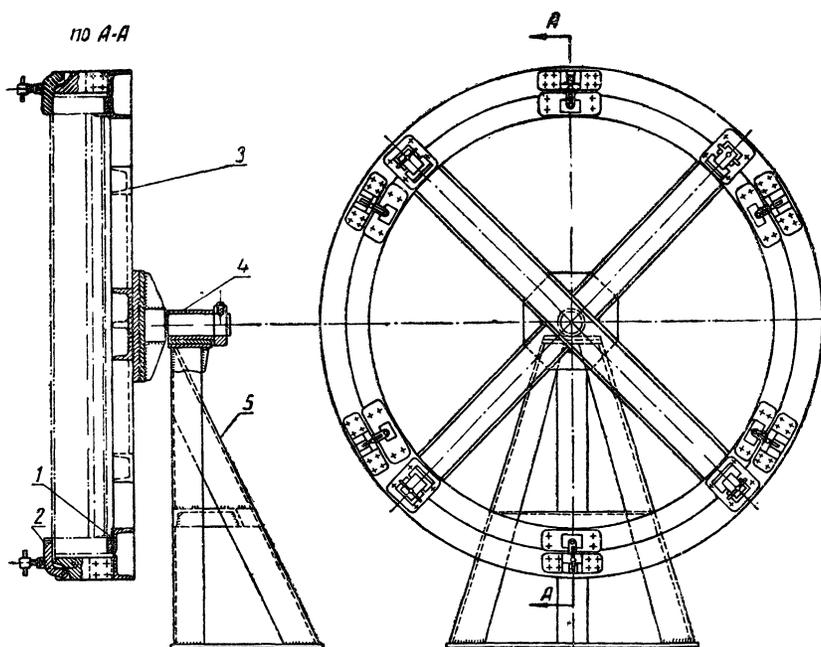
Приспособление для сборки и прихватки бензобака.
